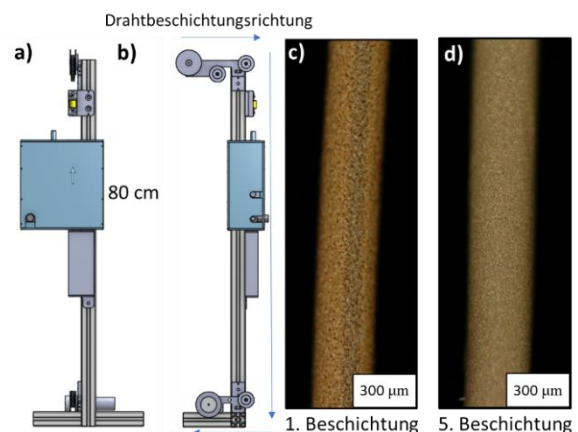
a) Drahtbeschichtungsanlage (vorne) b) Drahtbeschichtungsanlage (links) c) einfach beschichteter Kupferdraht d) 5-fach beschichteter Kupferdraht
